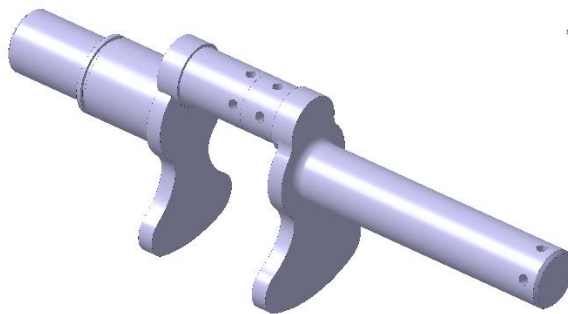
imagen del resultado de cómo deben quedar acoplados los cigüeñales. A la izquierda el cigüeñal 1 y a la derecha el cigüeñal 2. En la parte central excéntrica debe ir el casquillo con los taladros.
